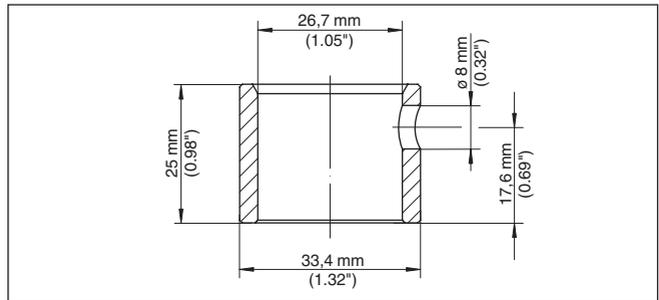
medidas luva para soldagem PMC 1" - VEGABAR 82
